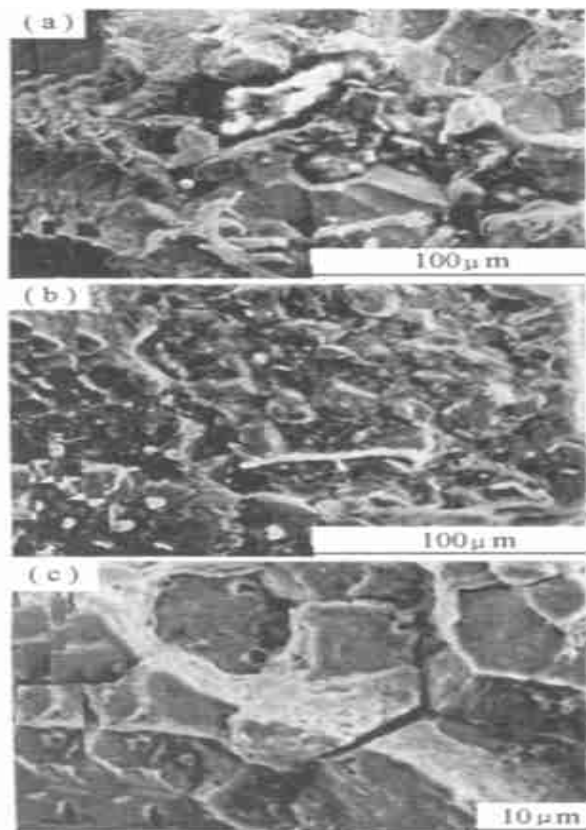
裂纹源 (a, b) 及沿晶断口 (b) 微观形貌
